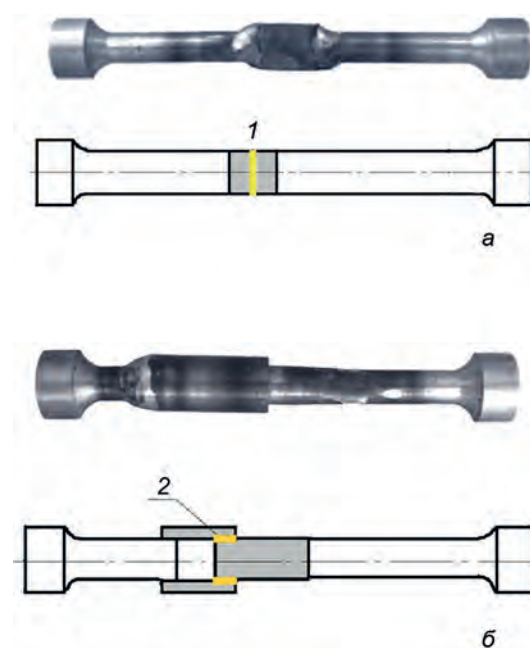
Образцы для испытаний и их эскизы: а – на разрыв; б – на срез; 1, 2 – швы деформационной сварки
